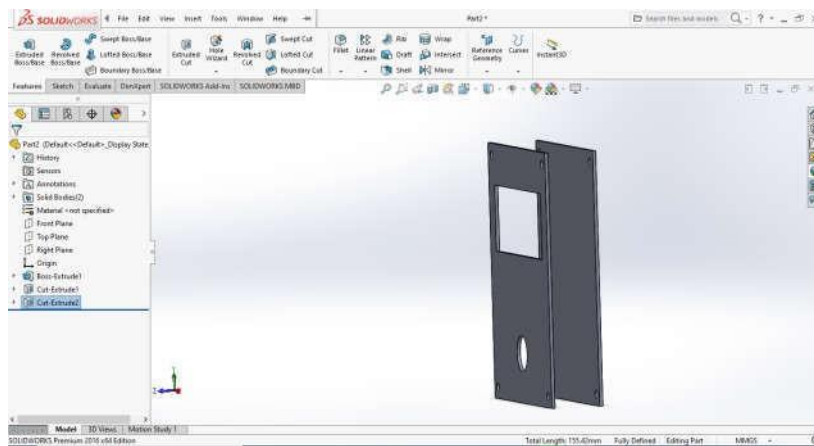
Part 4 - Sketch untuk melubangi part
